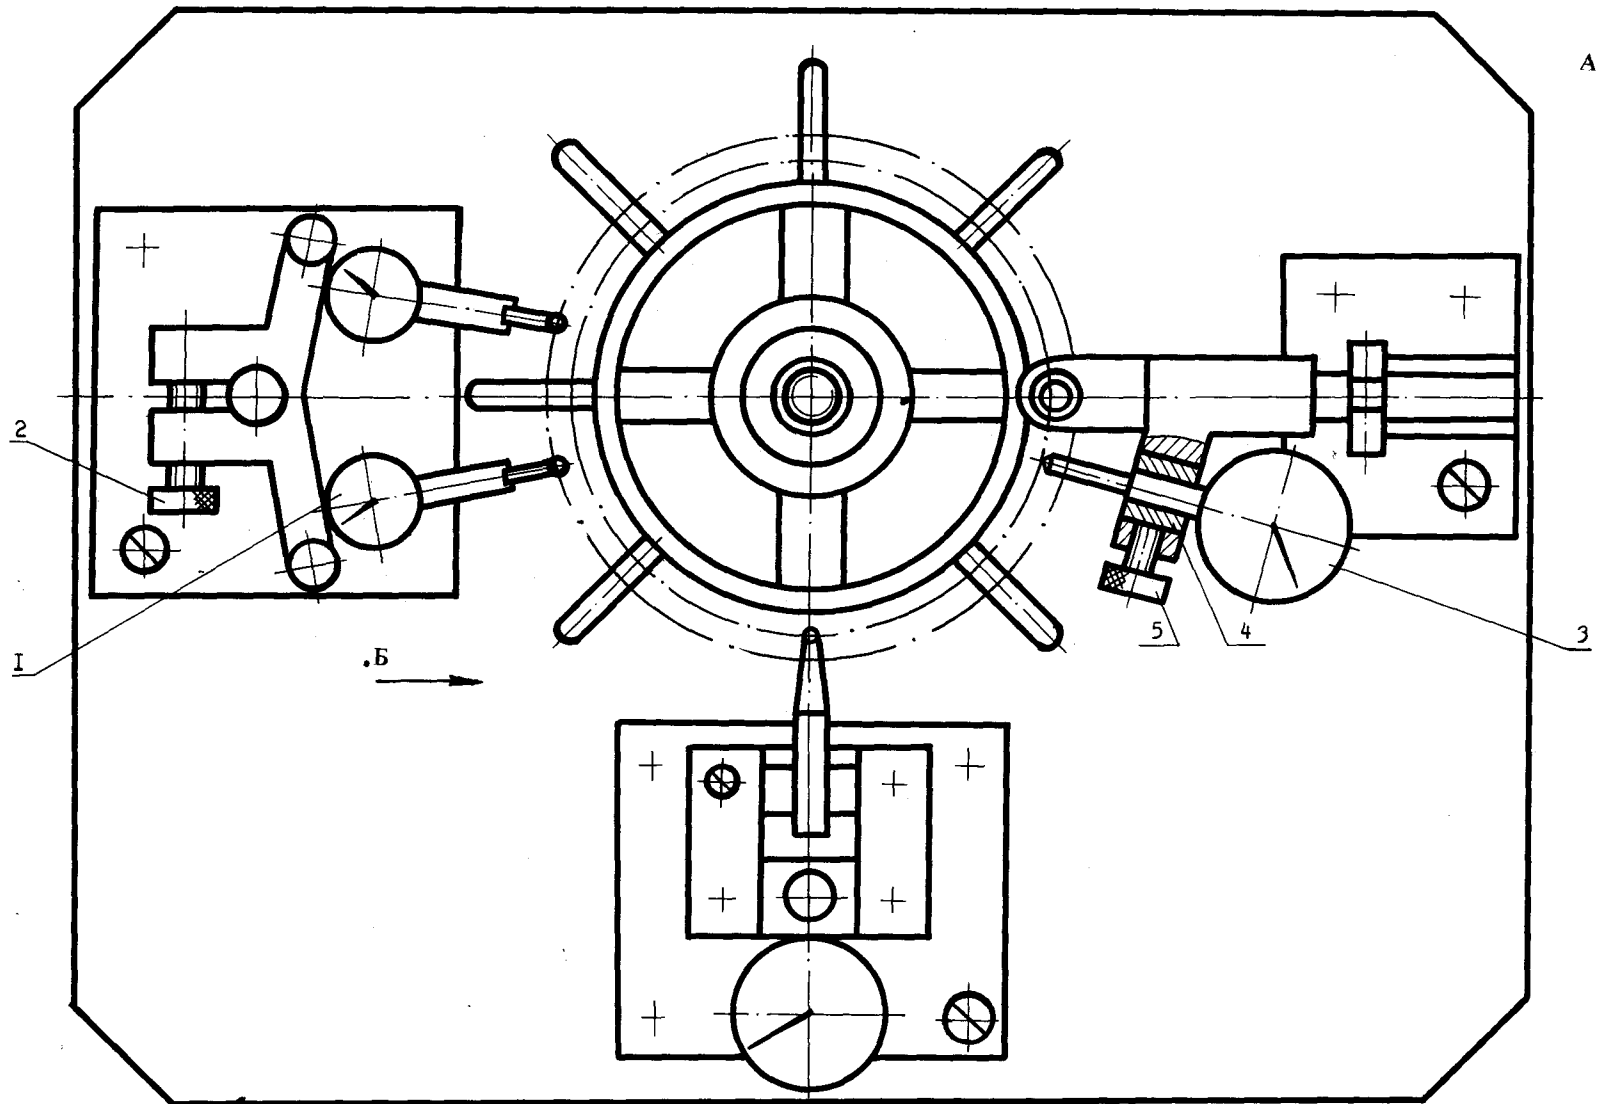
Контрольное приспособление для проверки торцового и радиального биений (вид А на рис. 2.1):
